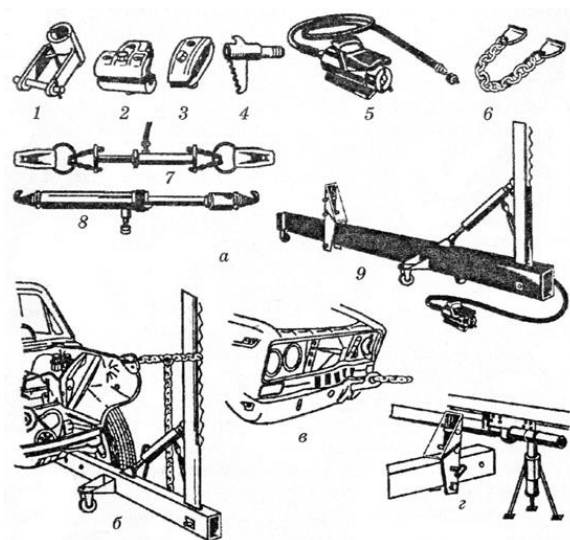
Приспособления для выполнения правки деформированного участка кузова:
